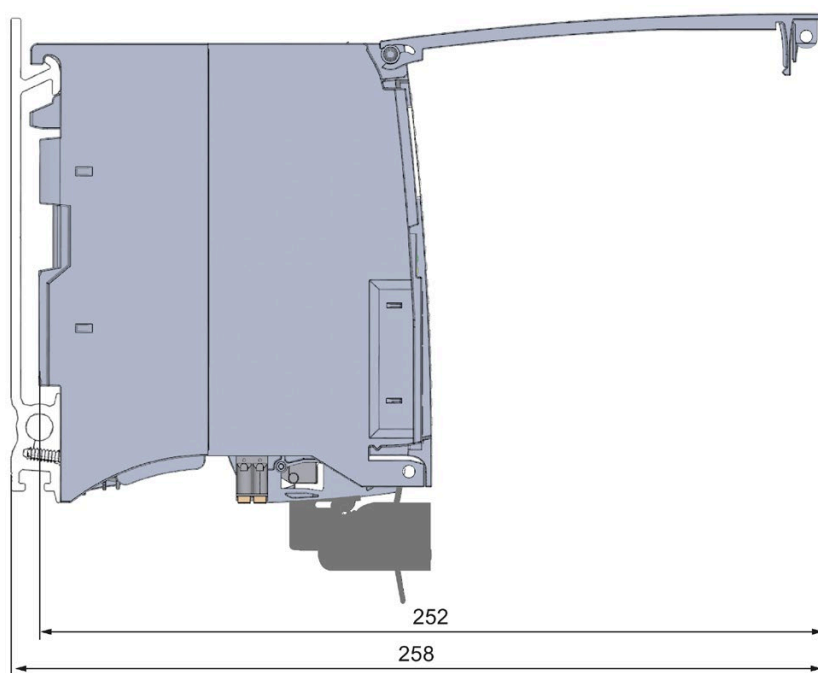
Maßbild der CPU 1512C-1 PN - Seitenansicht mit geöffneter Frontklappe
